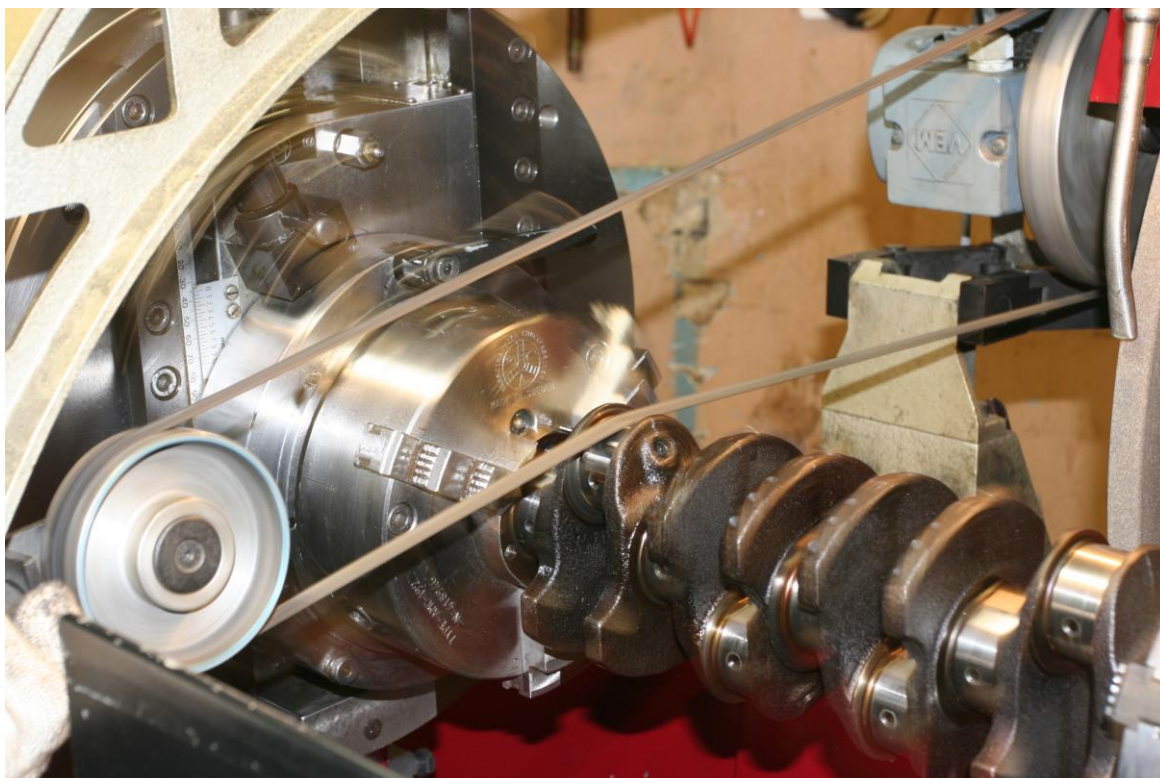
Выполнить полировку соосных шеек, используя полировальное приспособление.
